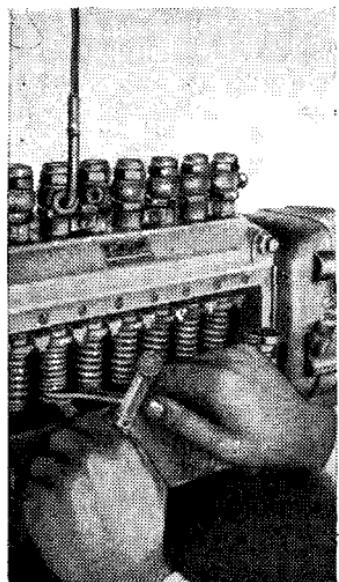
Установка начала подачи топлива регулировочным болтом толкателя
